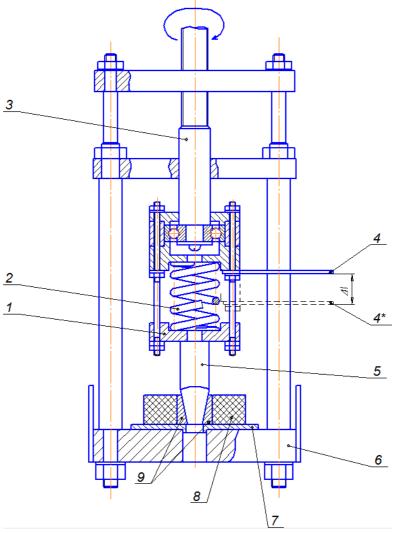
Устройство для разрыва дисков: 1— нижняя опора пружинного блока, 2 — пружина, 3 — вал, 4 - замерная планка в исходном положении, 4* — замерная планка в момент разрушения образца, 5 — клин, 6 — Основание (круг), 7 — пластина для сборки, 8 — образец породы, 9 — матрица.
